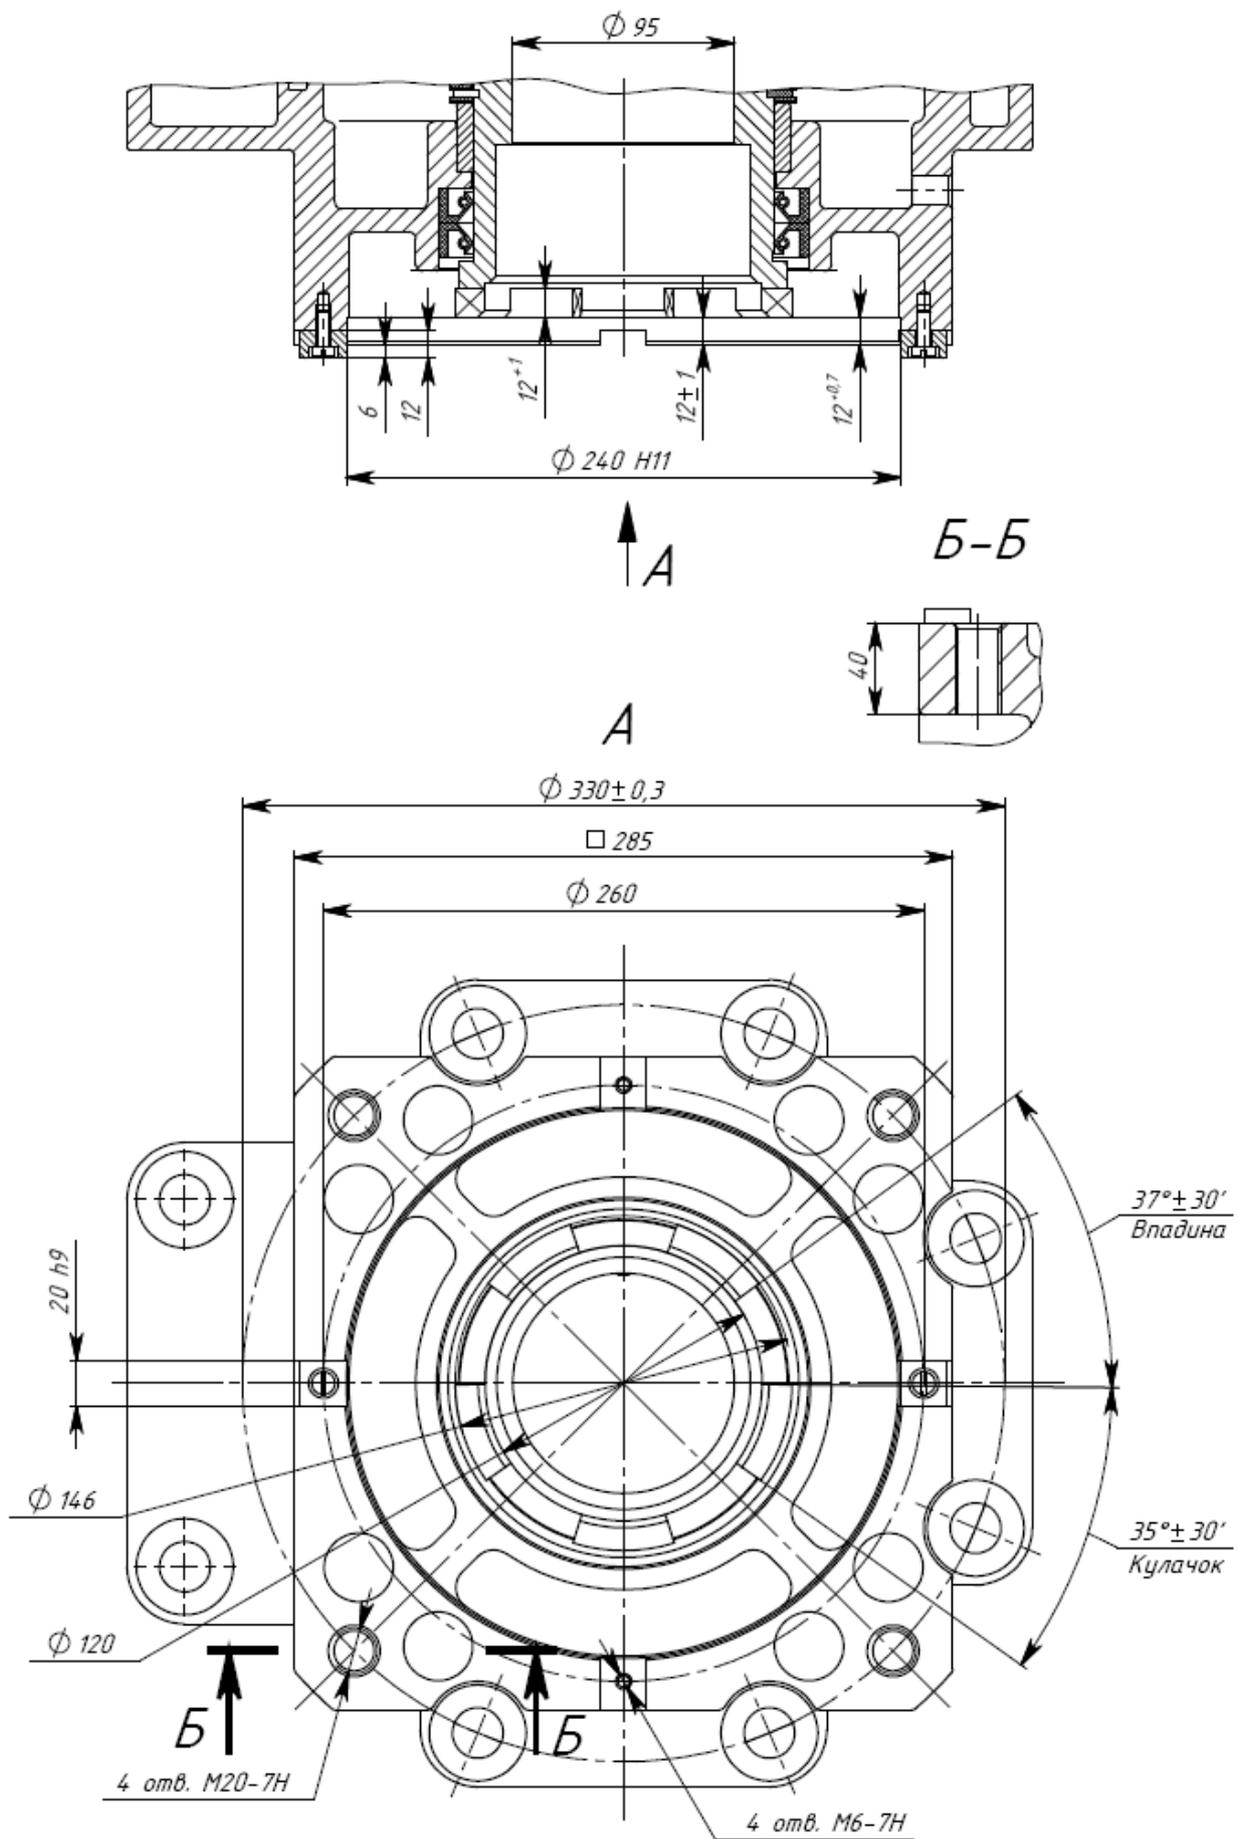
Присоединение типа Г для конструктивной схемы 43
